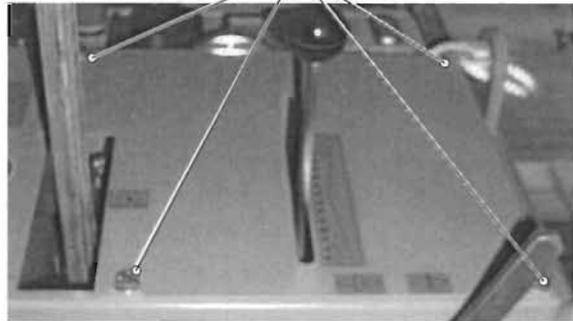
CF•50.2 Е, Защитная решетка снята с корпуса
